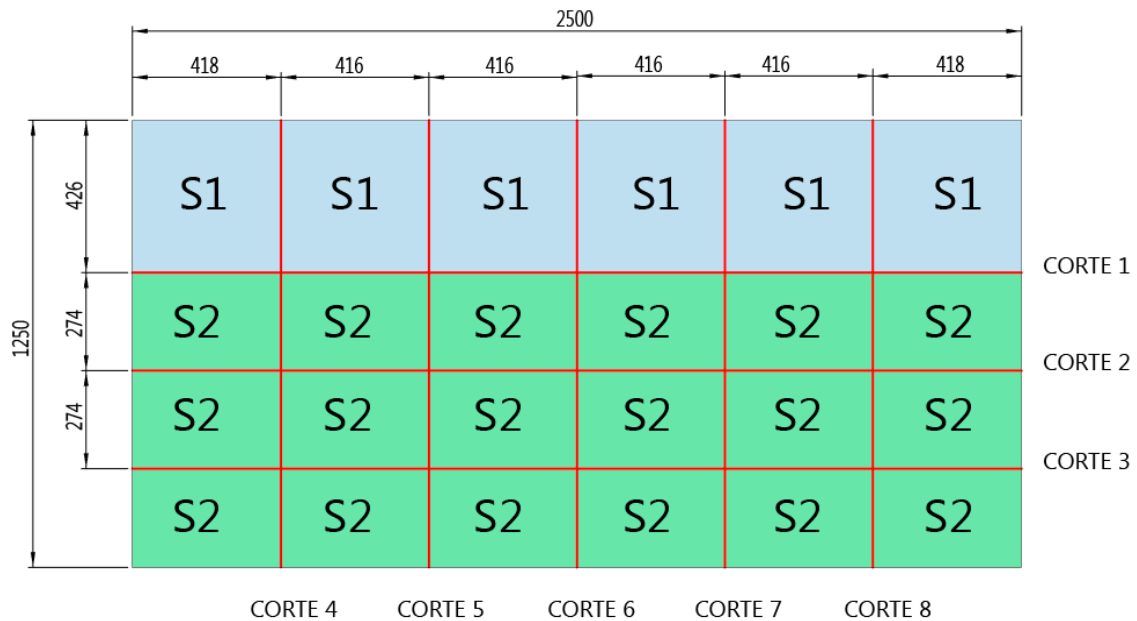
Distribución 2 corte tablero. Elaboración propia
